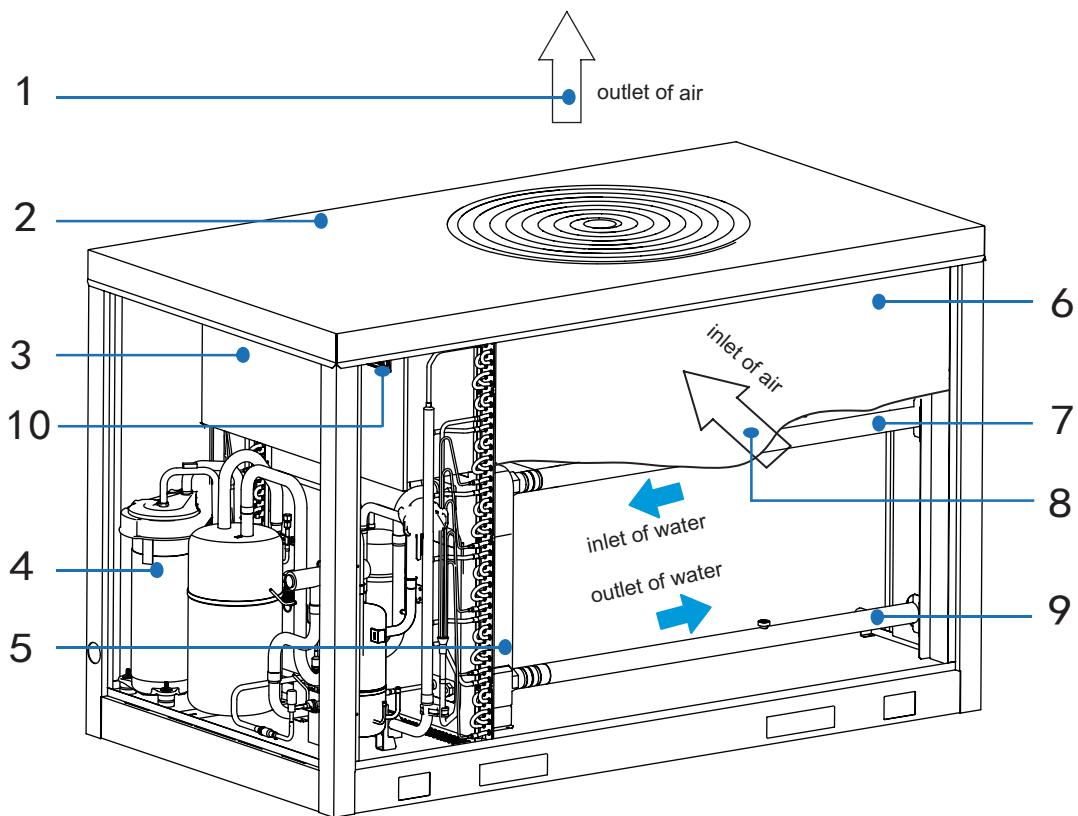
Componenti principali dell'unità KEM-30 DNS3
